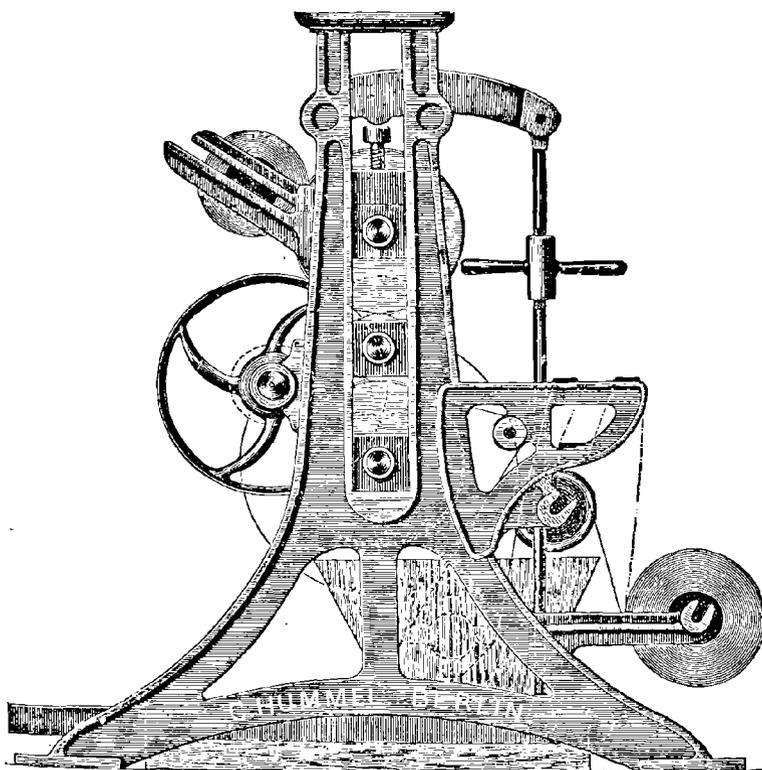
Machine à apprêter avec trois rouleaux et vis élargisseuse.
